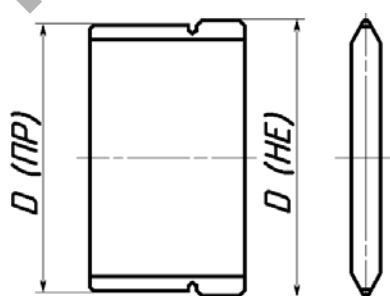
Калибр-пробка для контроля длины паза
